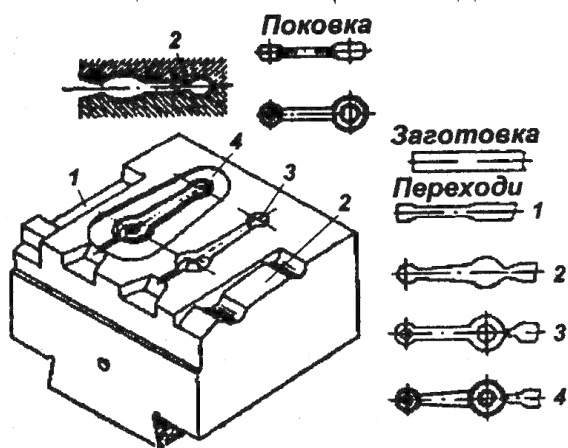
Переходи і загальний вид штампа для кування шатуна:
